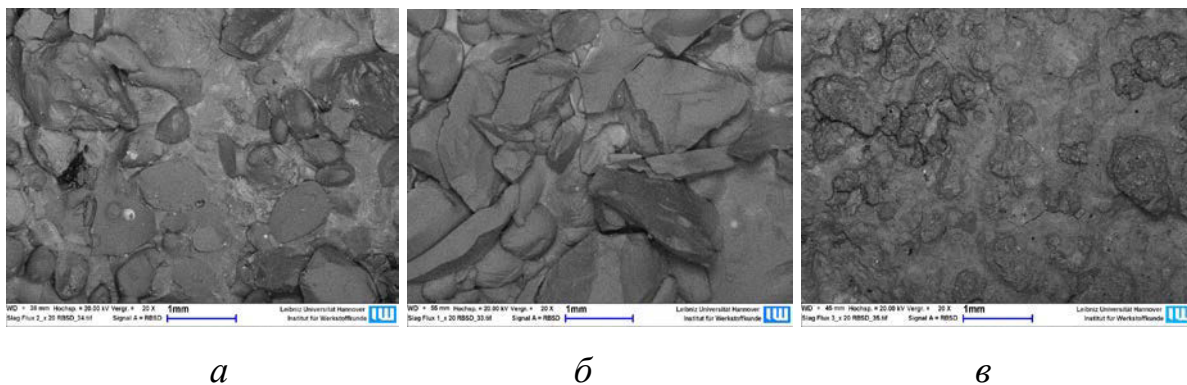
Внешняя поверхность сварочной корки (x20): а) шлак габбро-диабазы; б) шлак горнблендита; в) шлак агломерированного флюса
